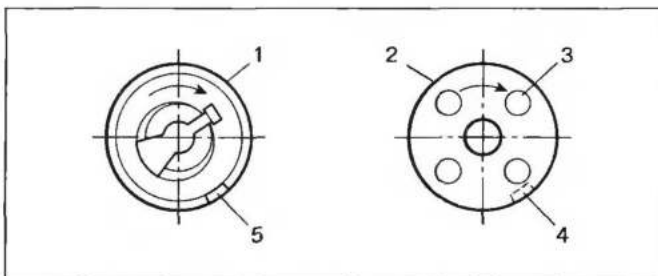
Установка распределителя зажигания (коленчатый вал установлен в положении ВМТ первого цилиндра): 1 — корпус распределителя; 2 — крышка; 3 — высоковольтный вывод свечи первого цилиндра (остальные провода соединяются согласно порядку работы цилиндров данного двигателя и направлению вращения ротора); 4 — шлиц на крышке; 5 — выступ на корпусе
